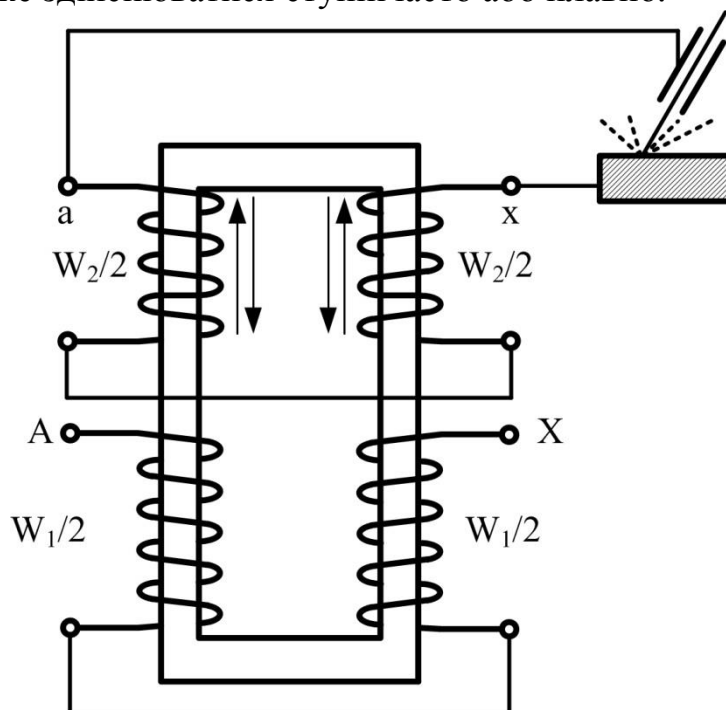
Схема вмикання зварювального трансформатора типу ТД (ТДМ)
